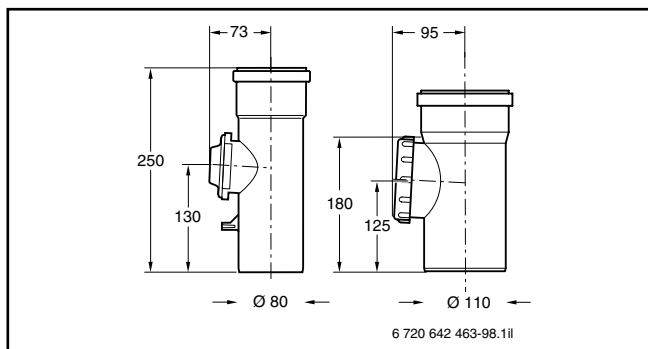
Tubo con apertura d'ispezione (misure in mm)
